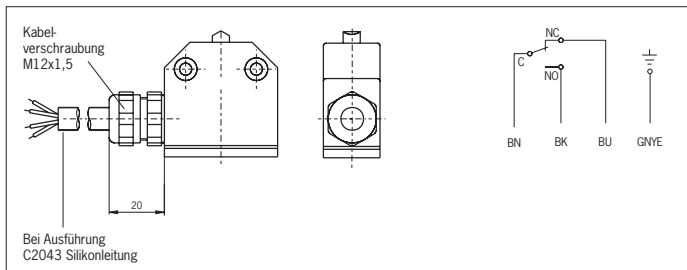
Maßzeichnung/Anschlussplan N01.550X... mit Anschlussleitung (PUR-Leitung, 4x0,5 mm²)
